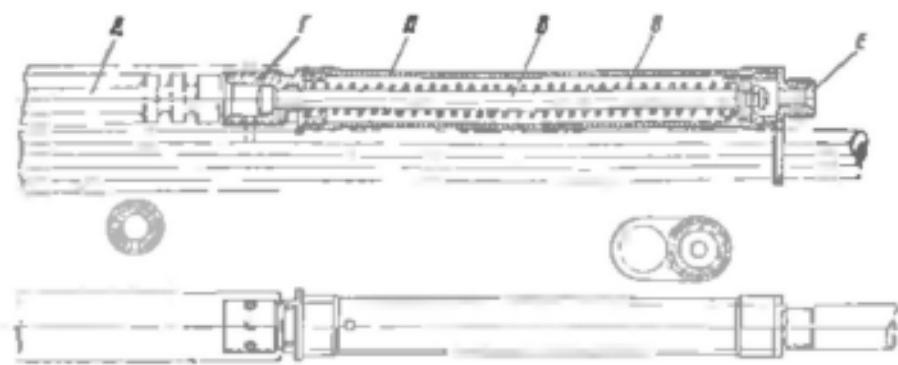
Цилиндр пневмоперезарядки пулемета ШКАС.
